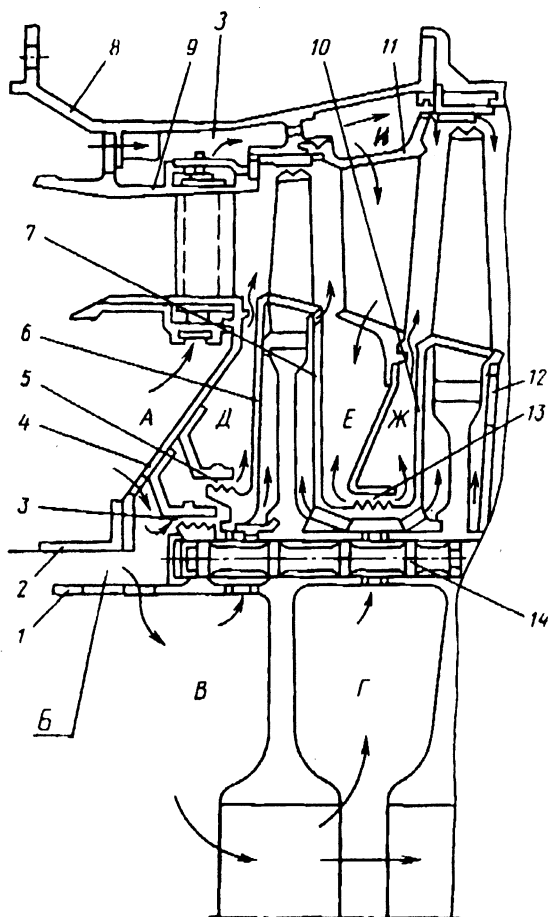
Схема охлаждения деталей турбины компрессора:
